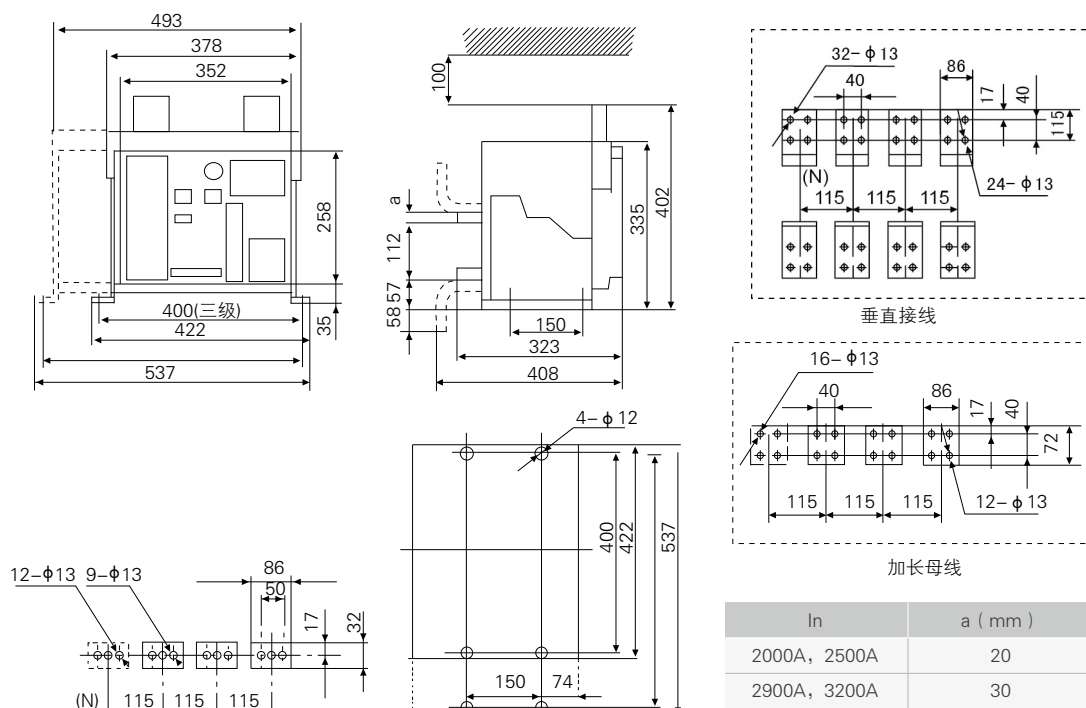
固定式断路器安装尺寸及外形尺寸 (BW1-3200)
